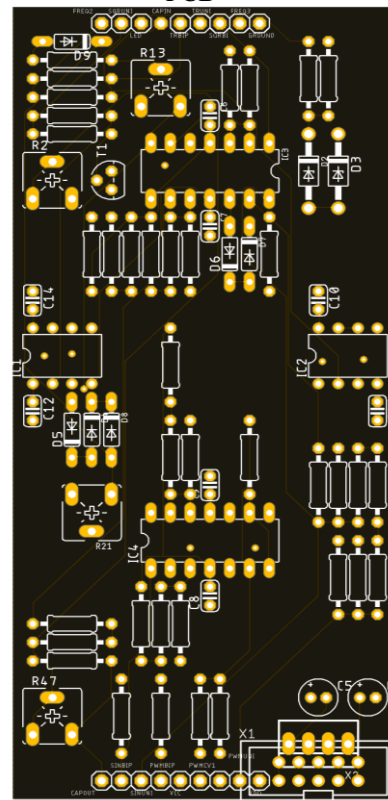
Board Layout: Pots&Sockets PCB
